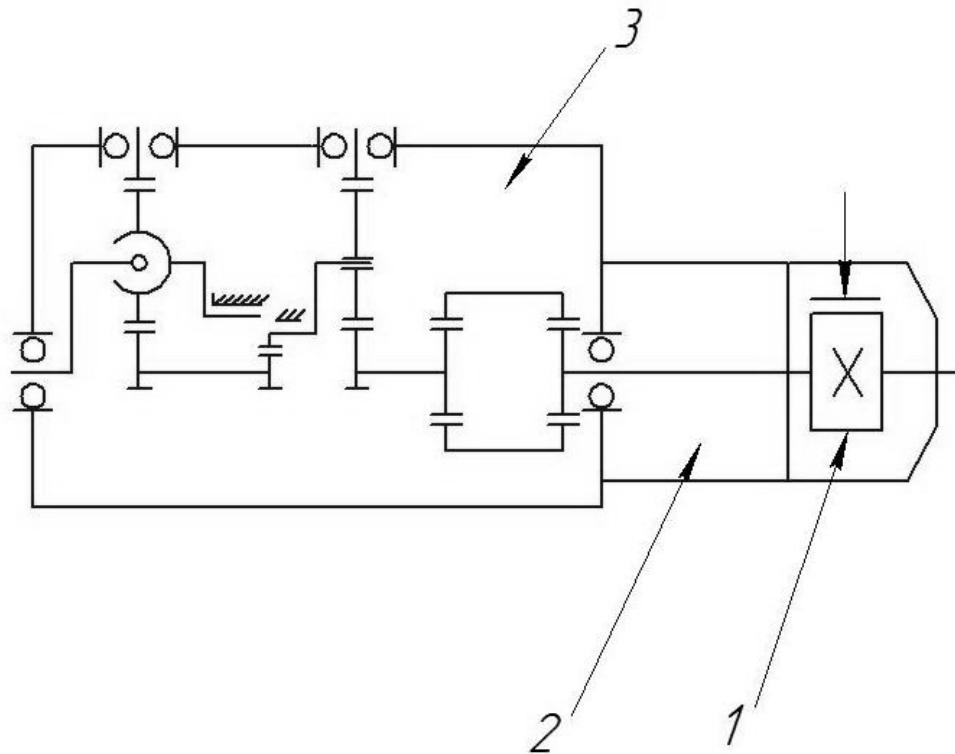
Кінематична схема мотор-редуктора типу ЗМП:
